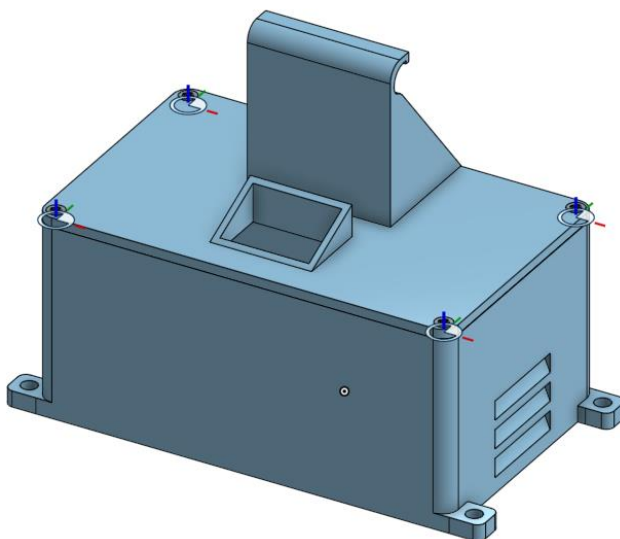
3D-модель основної частини корпусу внутрішнього блоку
